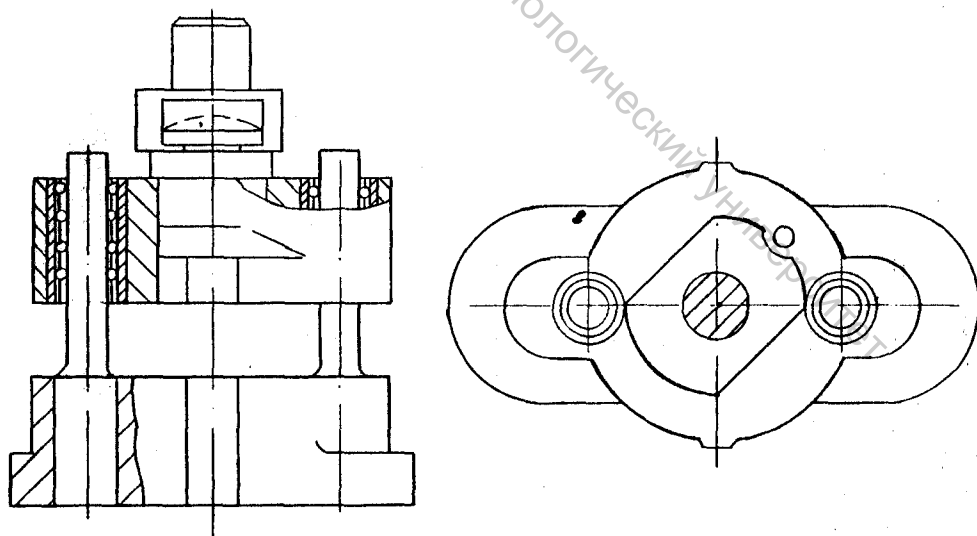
Прецизионный стандартный блок с осевым расположением направляющих колонок.
